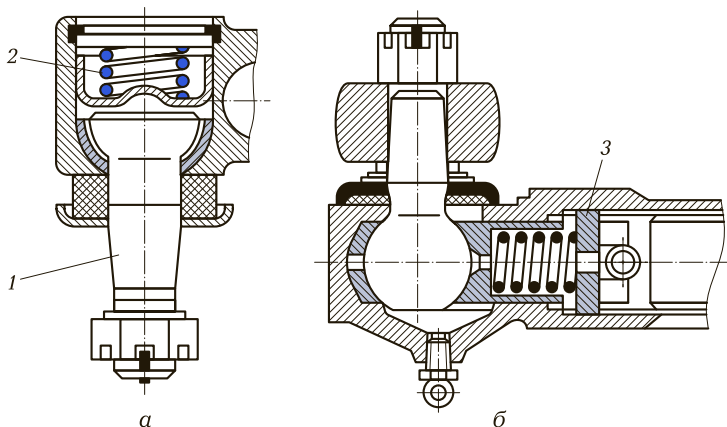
Устройство шарниров рулевых тяг с регулированием зазора: а — автоматическим; б — с помощью пружины; 1 — шаровой палец; 2 — пружина; 3 — гайка
